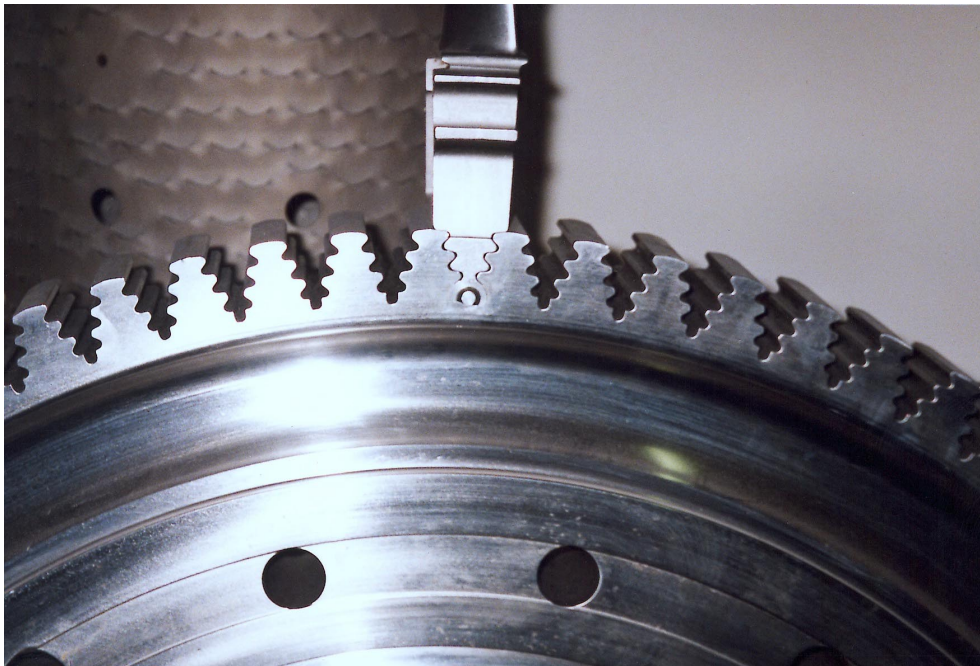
Tannenbaumförmige Schaufelbefestigung
